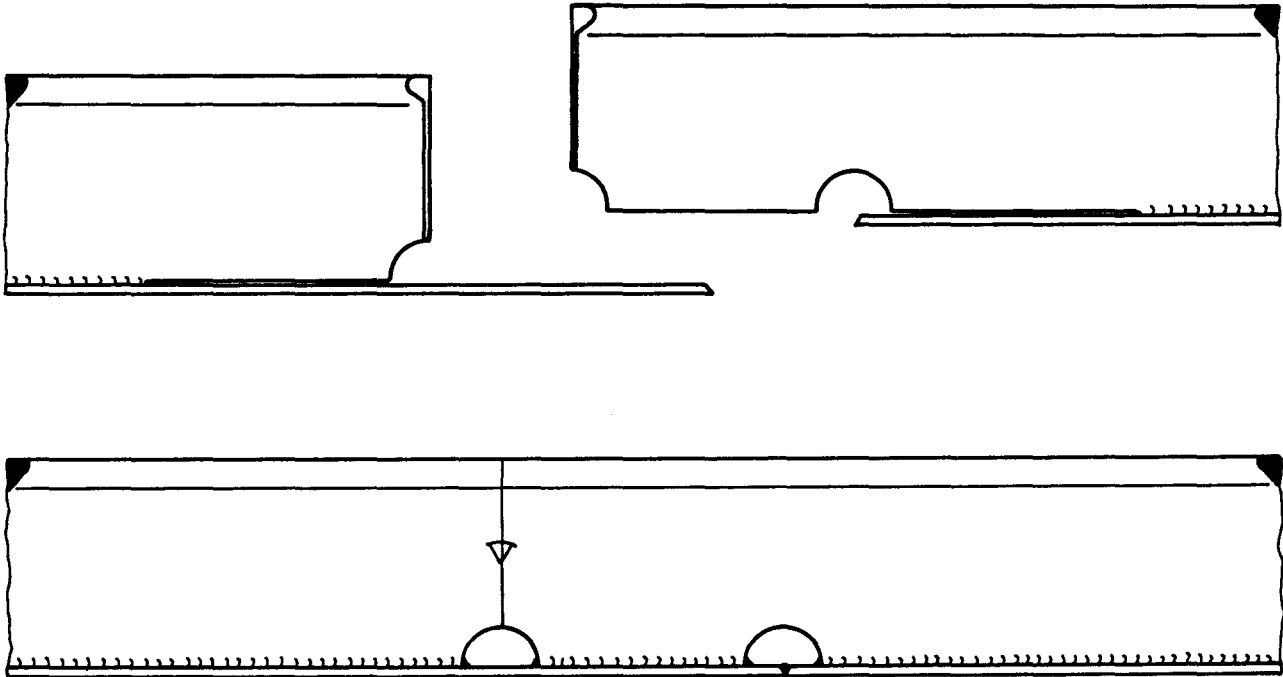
Profil- und Plattenstoß (übliche Bauweisen)
